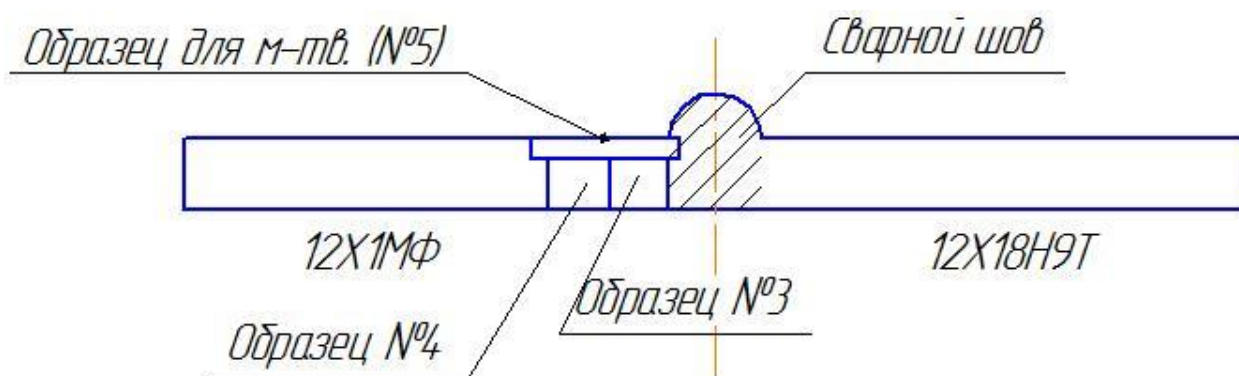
Схема сварного узла и вырезки образцов
